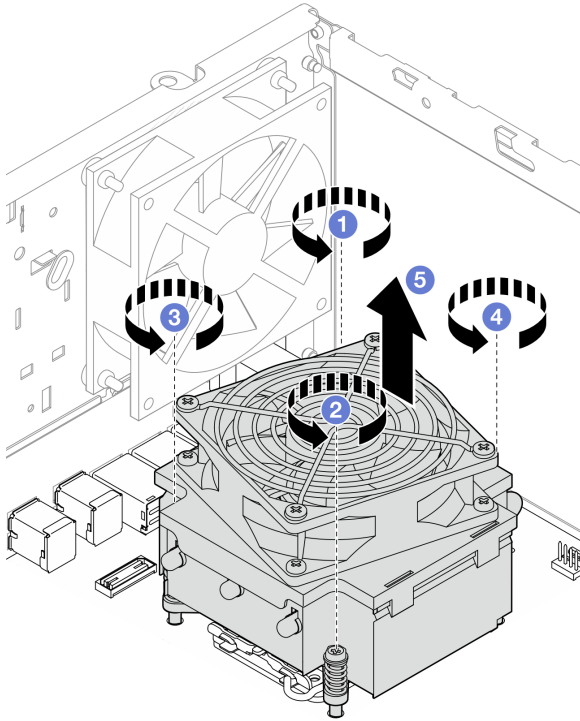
Lösen der Schrauben am Kühlkörper und Lüftermodul für Prozessoren mit einem TDP kleiner 95 W
